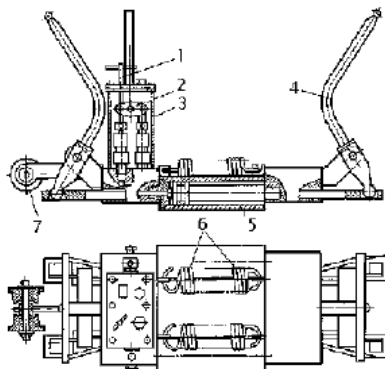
Гидравлический разгоночный прибор РН-03 [7]: 1 – спускной вентиль; 2 – плунжерный насос; 3 – резервуар с маслом; 4 – рычаги; 5 – распорный цилиндр; 6 – пружина; 7 – ролик; 8 – зажимные клинья
